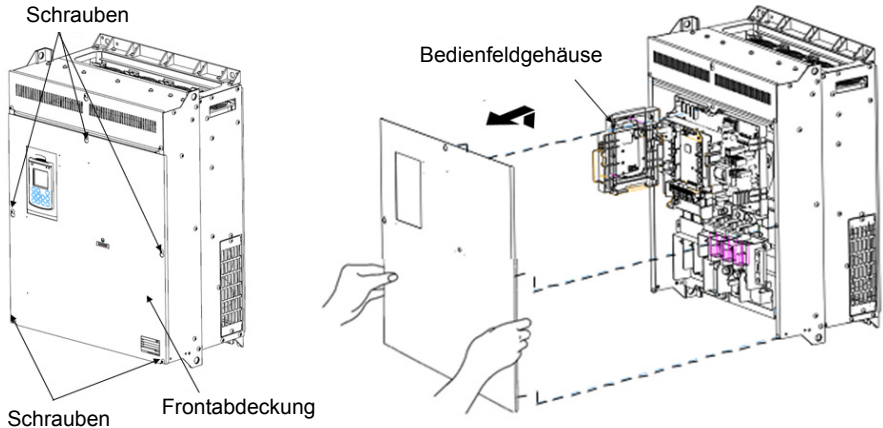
Entfernen der Frontabdeckung und des Klemmenblocks (FRN110AR1S-4□)
